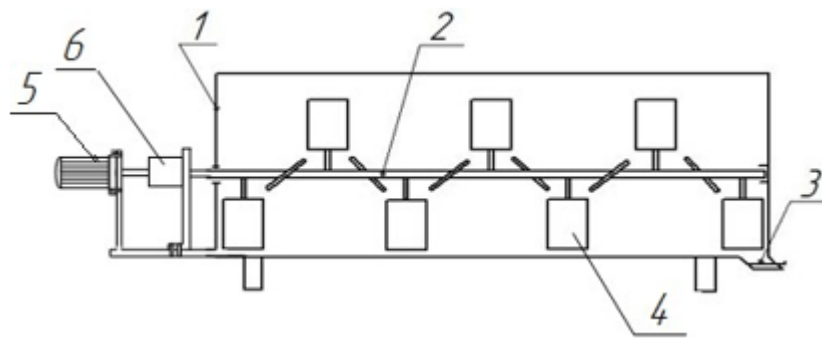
Схема лопатевого змішувача: 1 – бункер; 2 – вал; 3 – вивантажувальна горловина; 4 – лопаті; 5 – електродвигун; 6 – редуктор.
